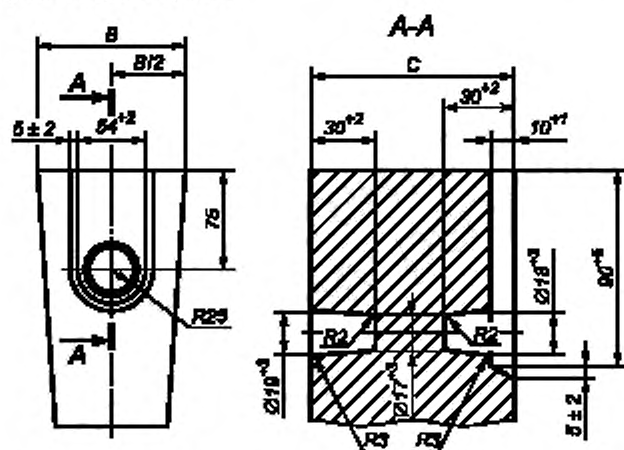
Размеры углублений для подвески. Вариант 1
